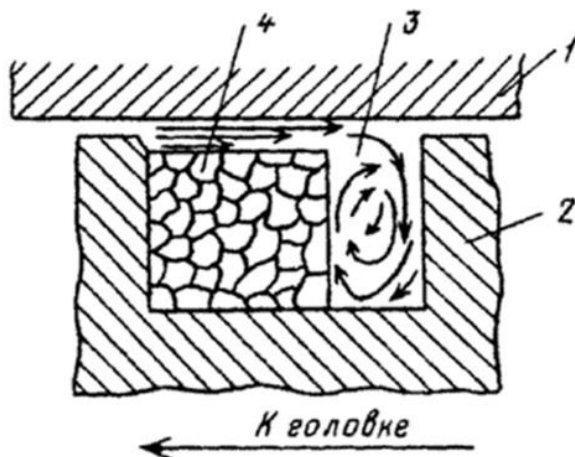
Схема плавления пробки материала в зоне II в межвитковом сечении шнека: 1 – стенки цилиндра; 2 – гребень шнека; 3 – потоки расплава полимера; 4 – спрессованный твердый полимер (пробка) в экструдере
